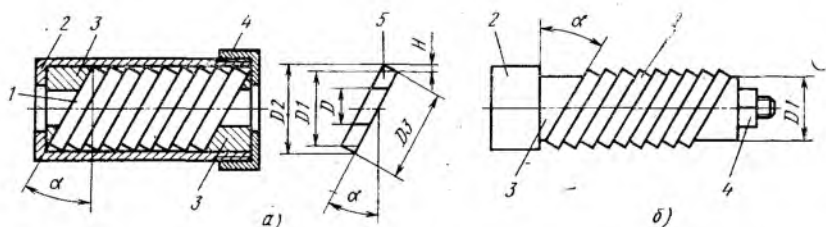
Приспособление для обработки фланцев со скошенными торцами
